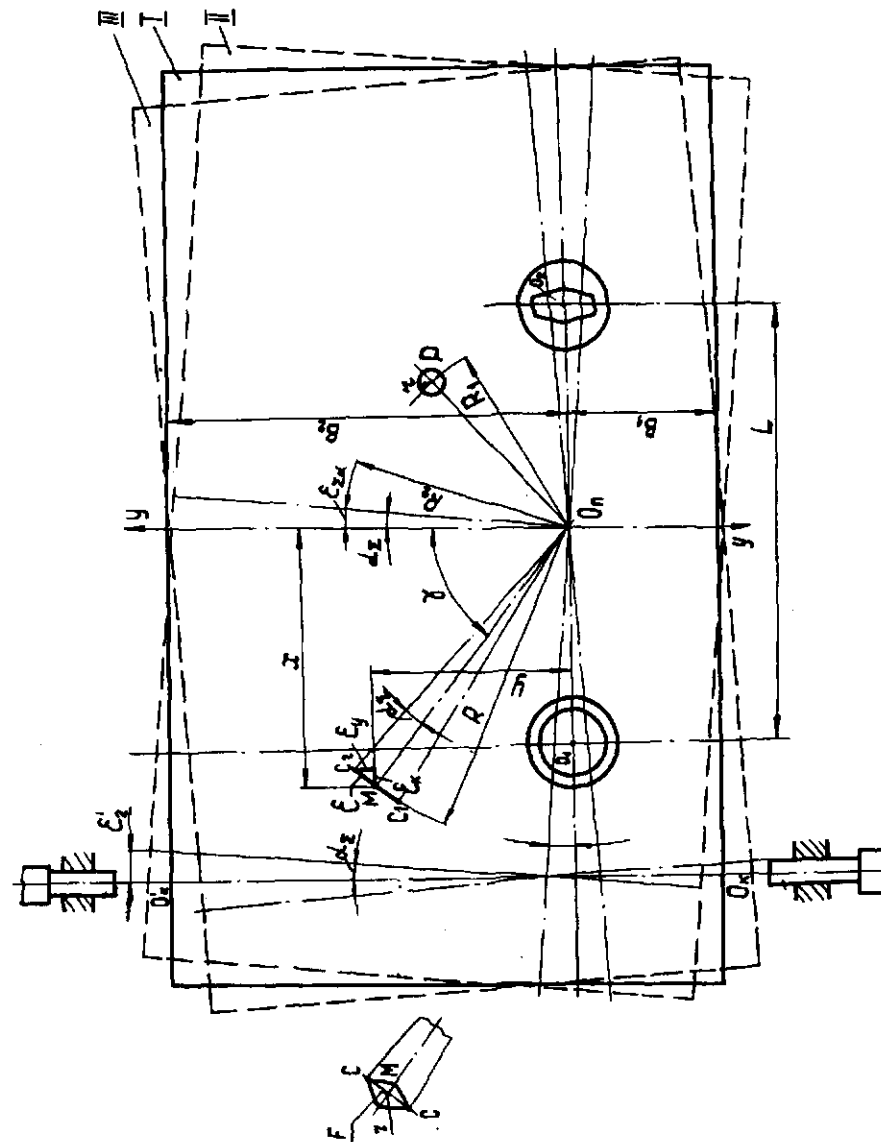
Схема влияния погрешности базирования заготовки на расположение осей отверстий
